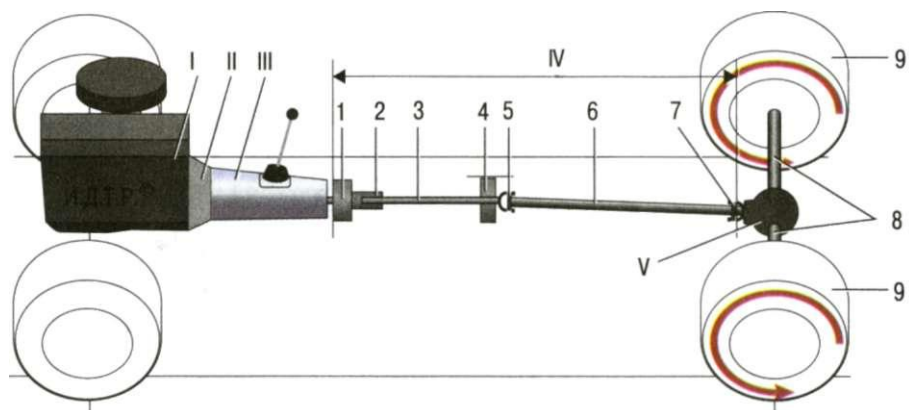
Схема трансмиссии заднеприводного автомобиля: I - двигатель; II - сцепление; III - коробка передач; IV - карданная передача: 1 - эластичная муфта; 2 - шлицевое соединение; 3 - передний карданный вал; 4 - подвесной подшипник; 5 - передний карданный шарнир; 6 - задний карданный шарнир; 7 - задний карданный шарнир; V - задний мост с главной передачей и дифференциалом: 8 - полуоси; 9 - ведущее (заднее) колесо
